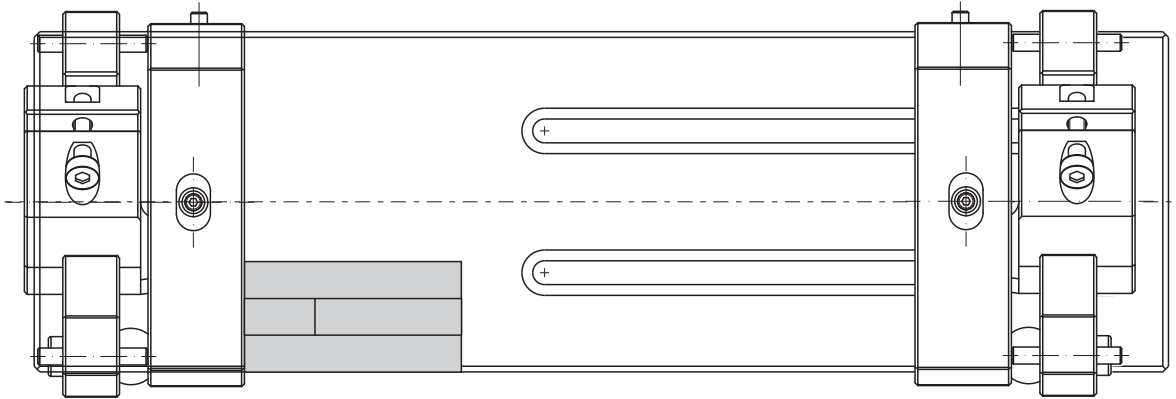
Ansicht Montageplatte und Montageadapter von oben, mit angelegtem Winkel
